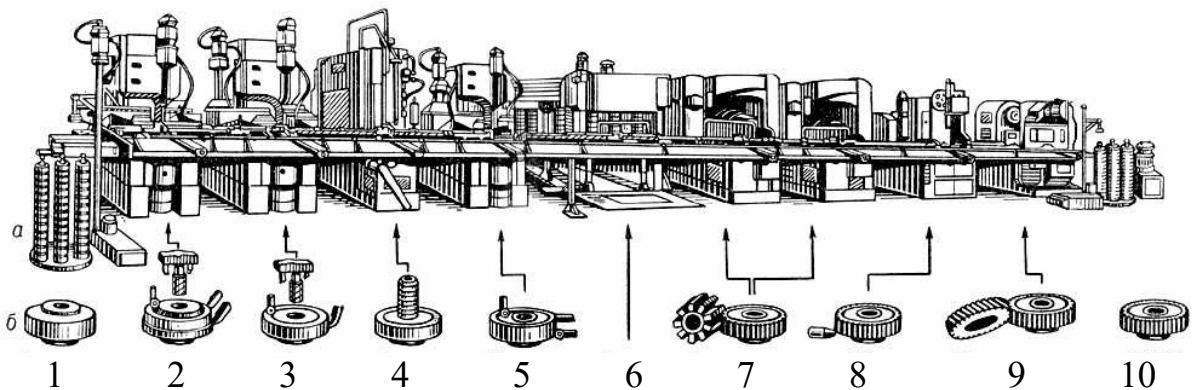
Автоматична лінія для обробки зубчастих коліс: а – загальний вигляд; б – технологічний процес: 1 – заготівка; 2 – I-а токарна операція; 3 – II-а токарна операція; 4 – протягування; 5 – чистова токарна операція; 6 – бункер; 7 – фрезерування; 8 – зубозаокруглення; 9 – шевінгування; 10 – готове зубчасте колесо
